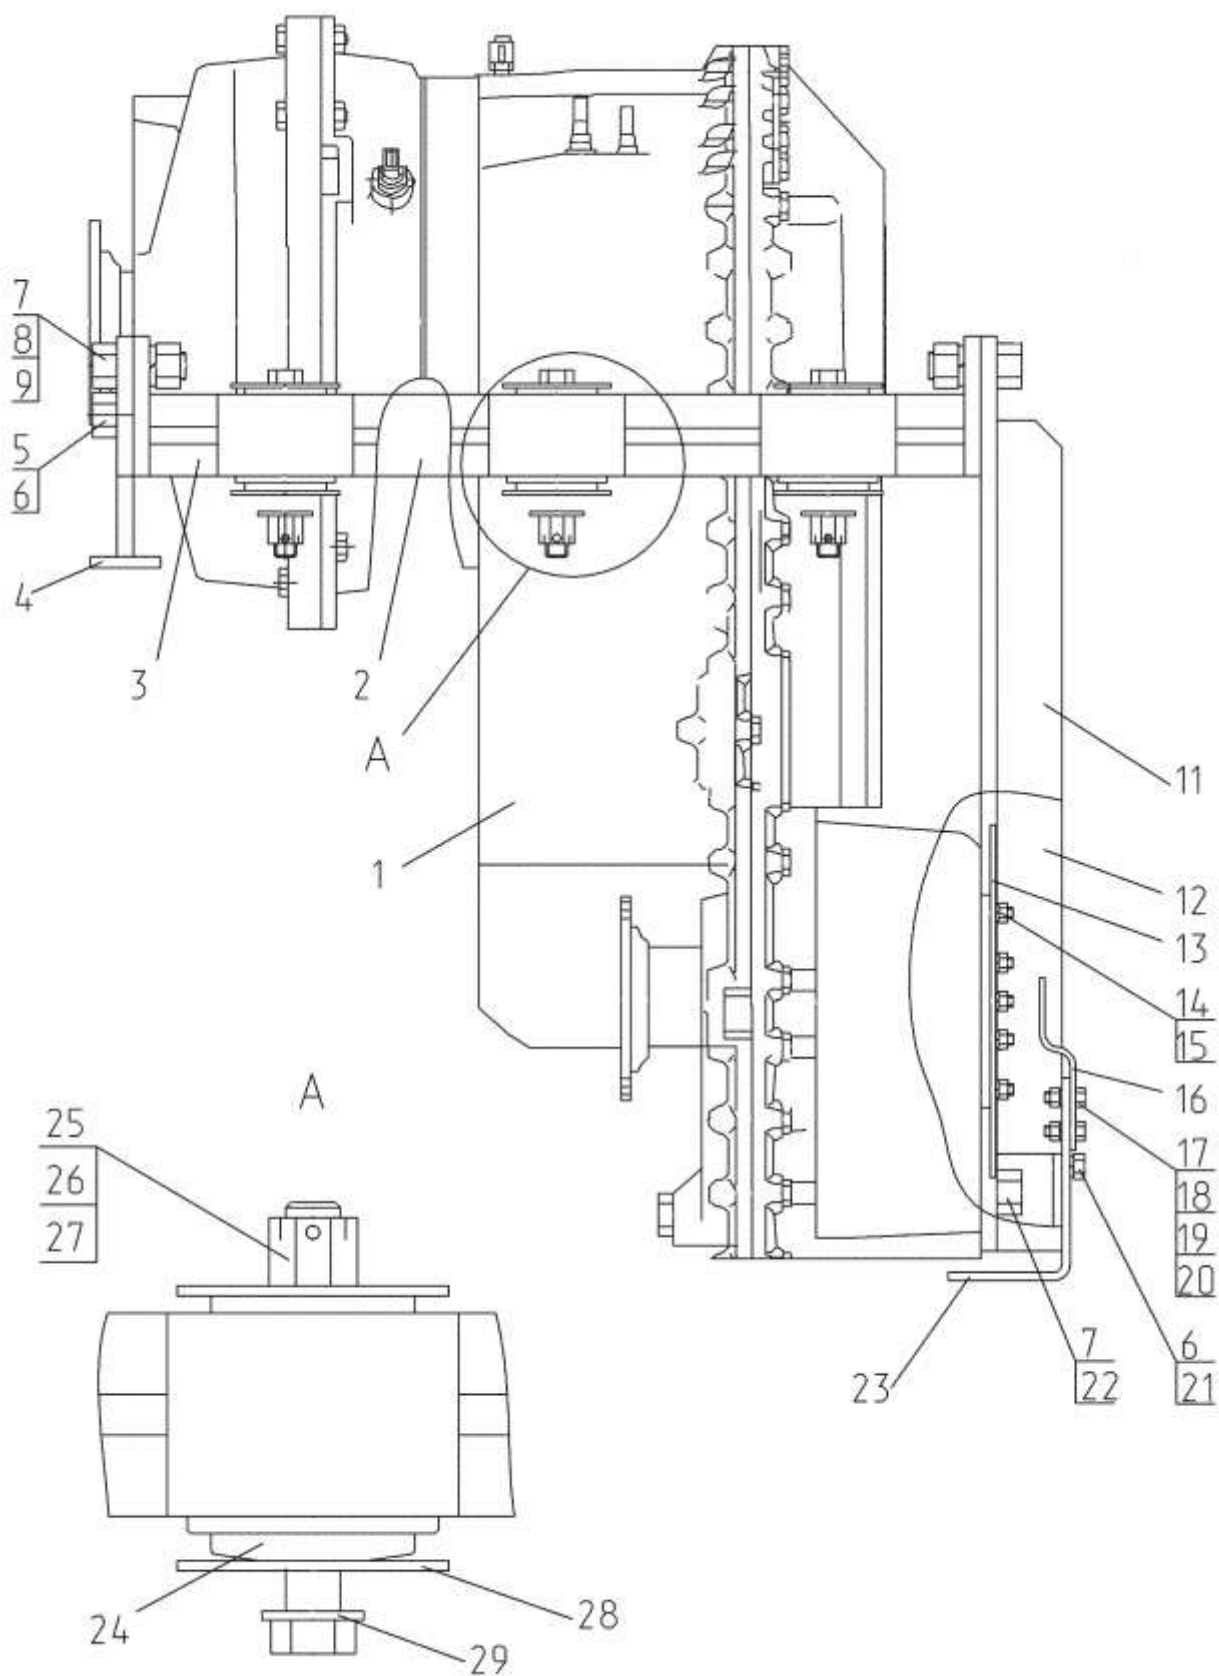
Установка коробки передач 723.03.02.00.000-01
